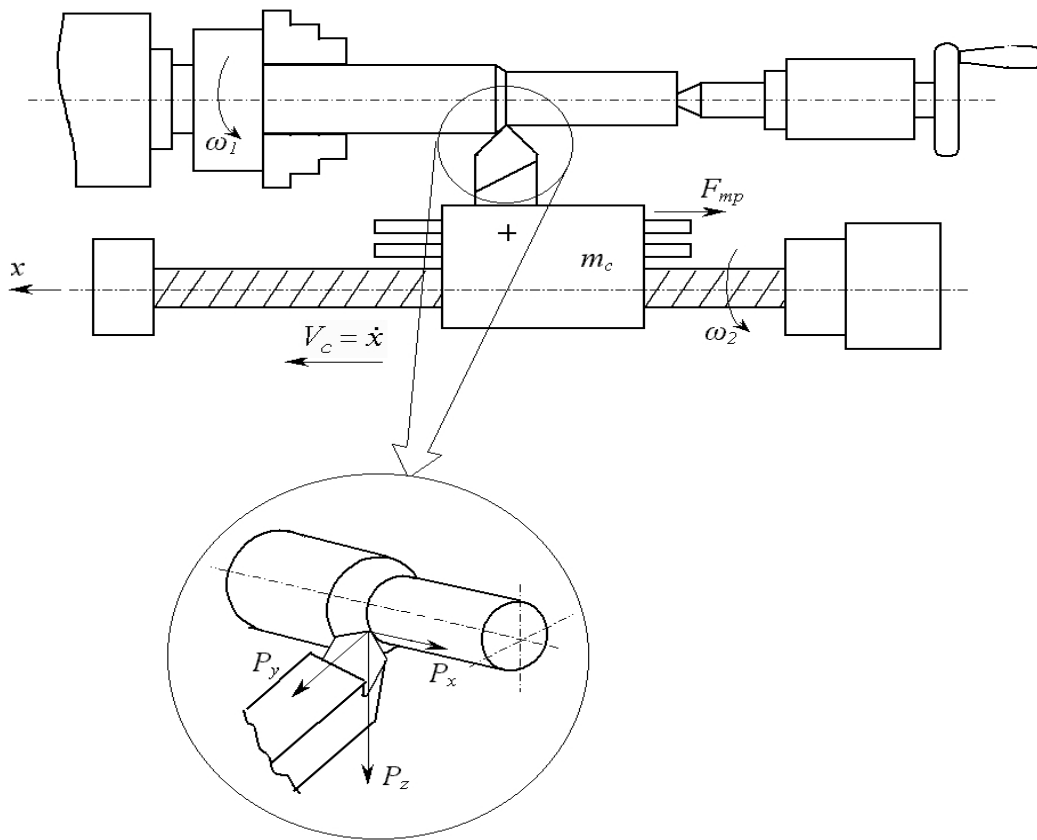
Конструктивная схема токарно-винторезного станка
